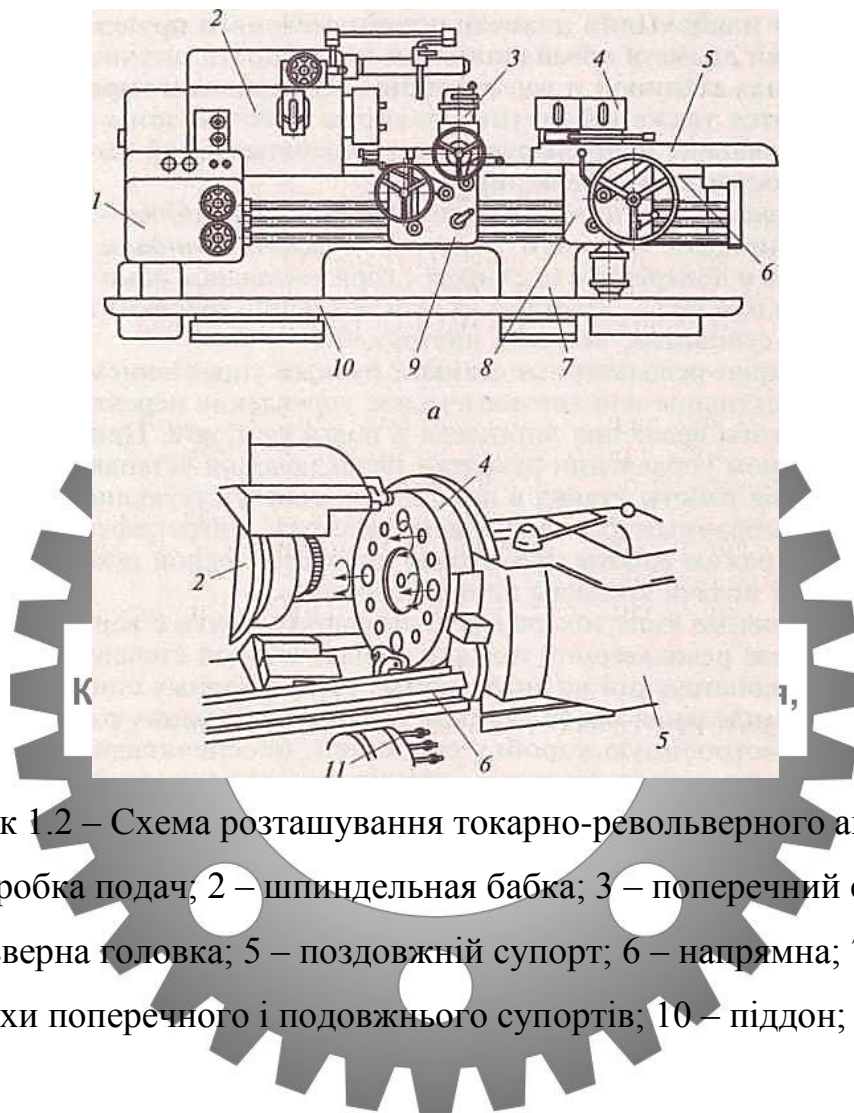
Схема розташування токарно-револьверного автомата:
